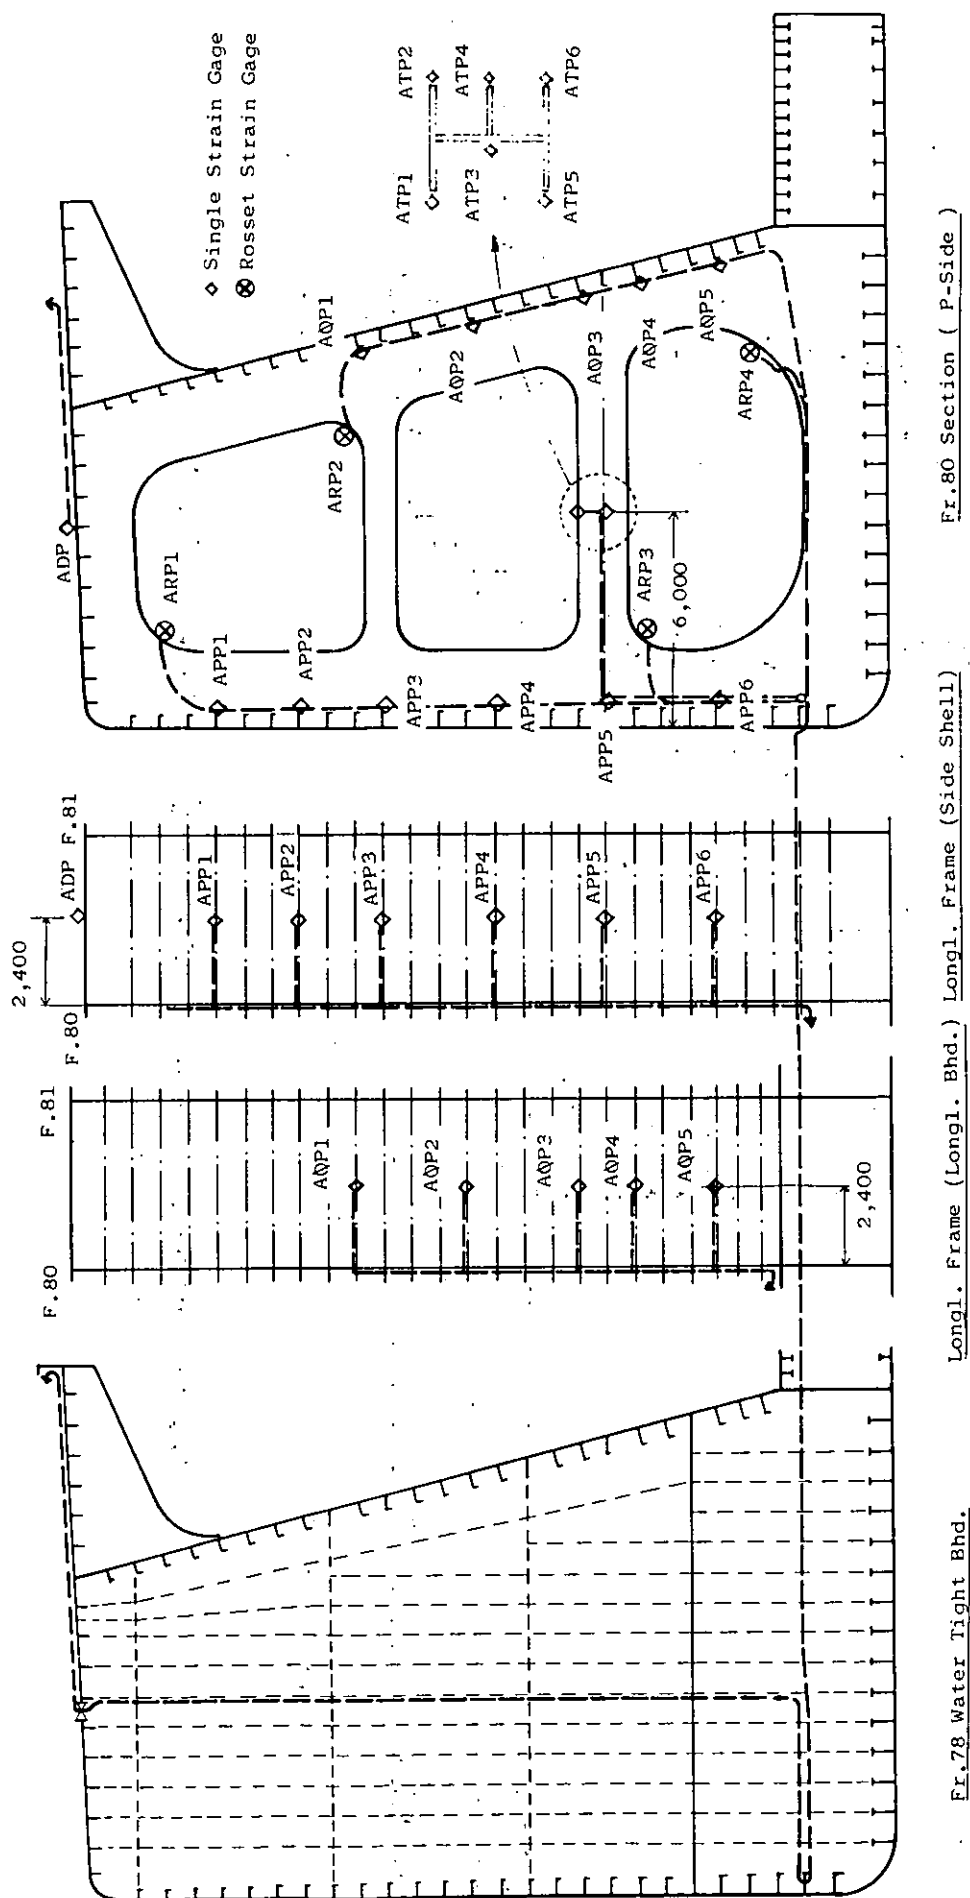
A断面 (Fr. 80 1/2) 至ゲージ配置図 (P-Side)
